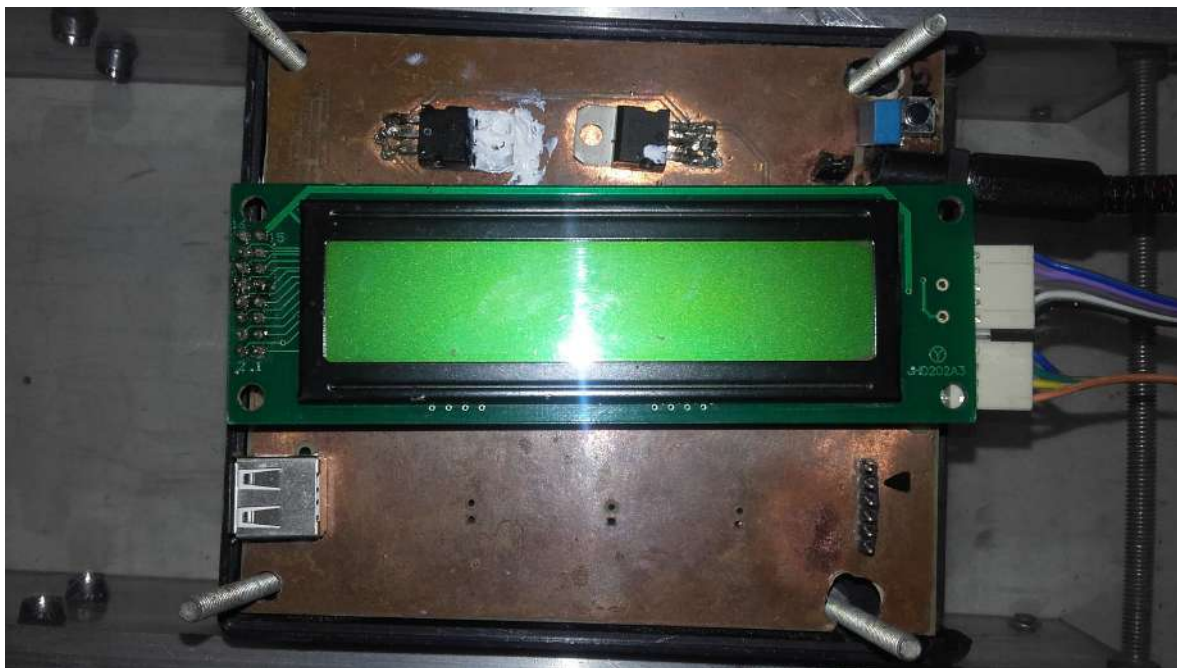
PCB soldada - vista por cima.* Fonte: Elaborada pelo autor.
